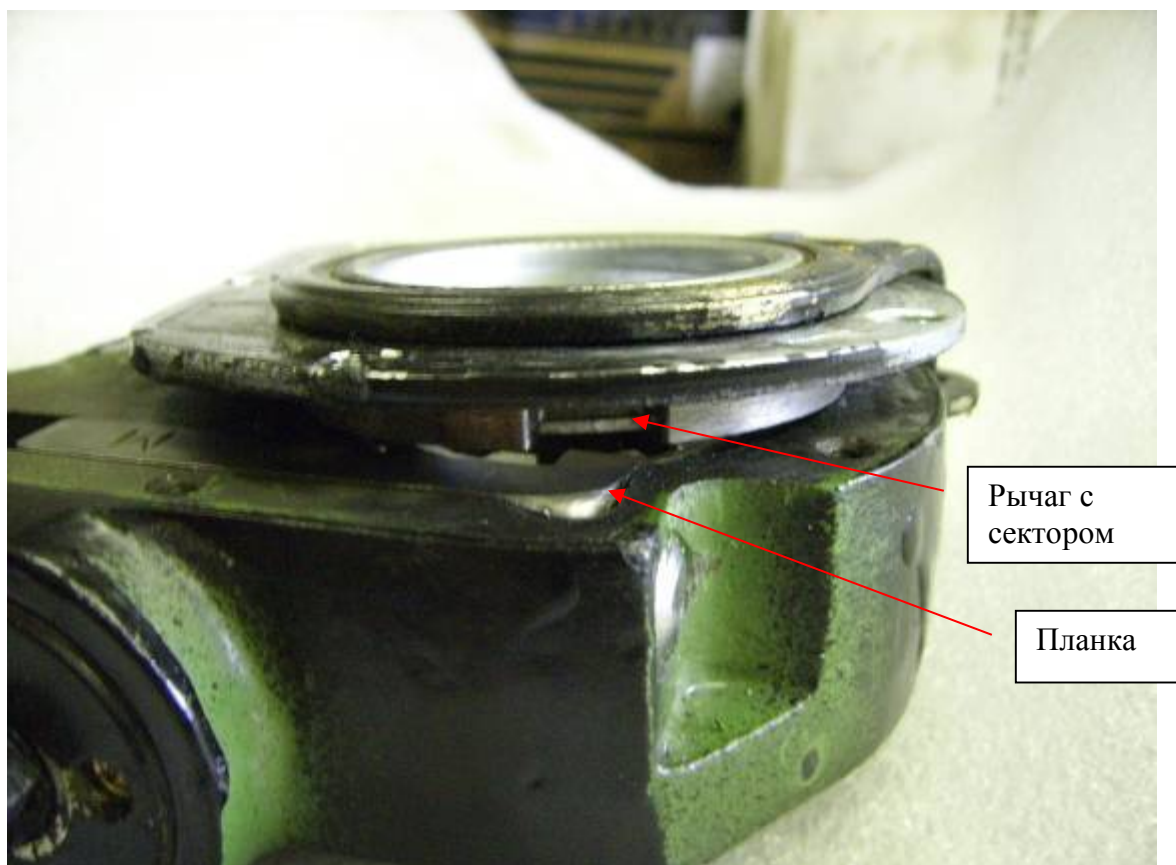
Взаимное положение планки храпового механизма и сектора опорного рычага
